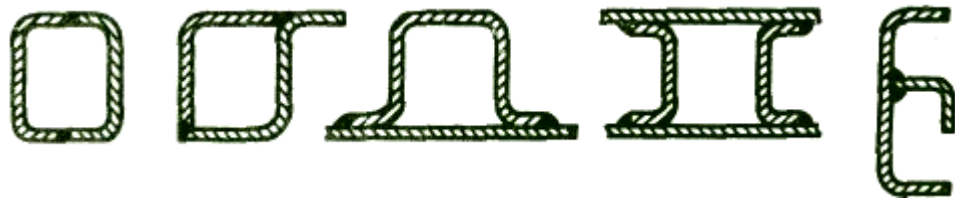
Жесткие сварные элементы из гнутых профилей
